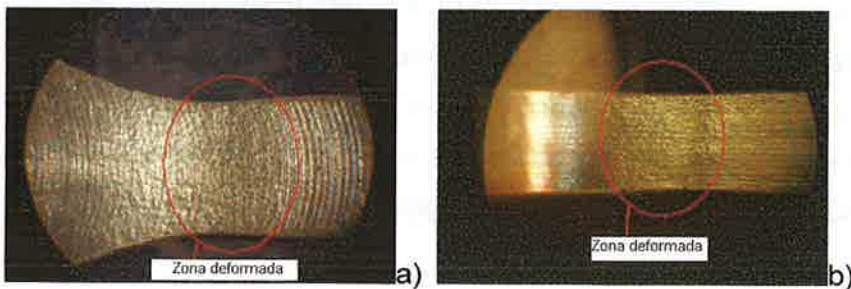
Uniones soldadas por fricción ensayadas en la barra Hopkinson a una velocidad de impacto de $v=18$ m/s.
